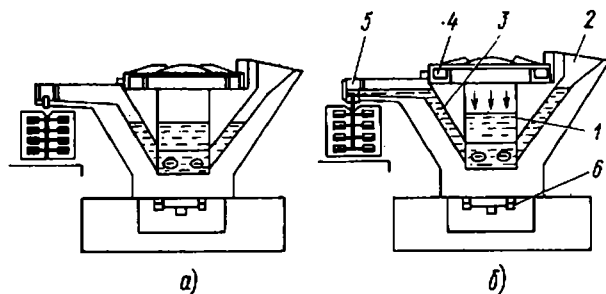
Схема пневматического дозатора для заливки чугуна:
